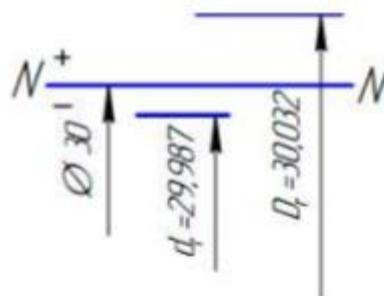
Схема расположения номинального и действительных размеров (отклонений) соединения
